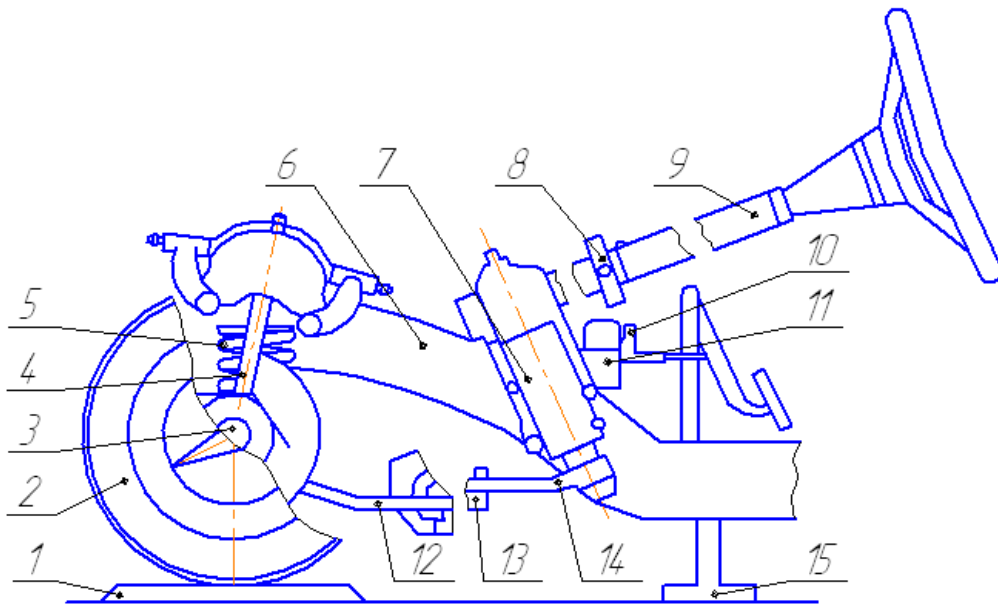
Установка для визначення параметрів рульового керування без підсилювача: 1 – поворотне коло; 2 – передній міст з колесами; 3 – поворотна цапфа; 4 – амортизатор; 5 – пружина; 6 – підрамник; 7 – рульовий механізм; 8 – муфта; 9 – вал; 10 – вакуумний підсилювач гальмової системи; 11 – головний гальмовий циліндр; 12 – рульовий важіль; 13 – шарніри рульових тяг; 14 – рульова сошка; 15 – підставка
